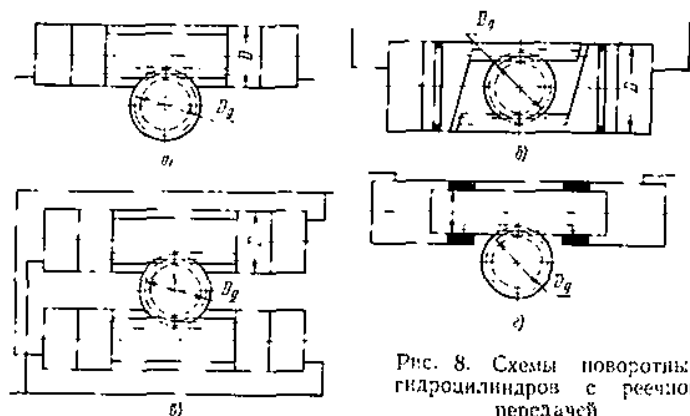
Схемы поворотных гидроцилиндров с реечной передачей
